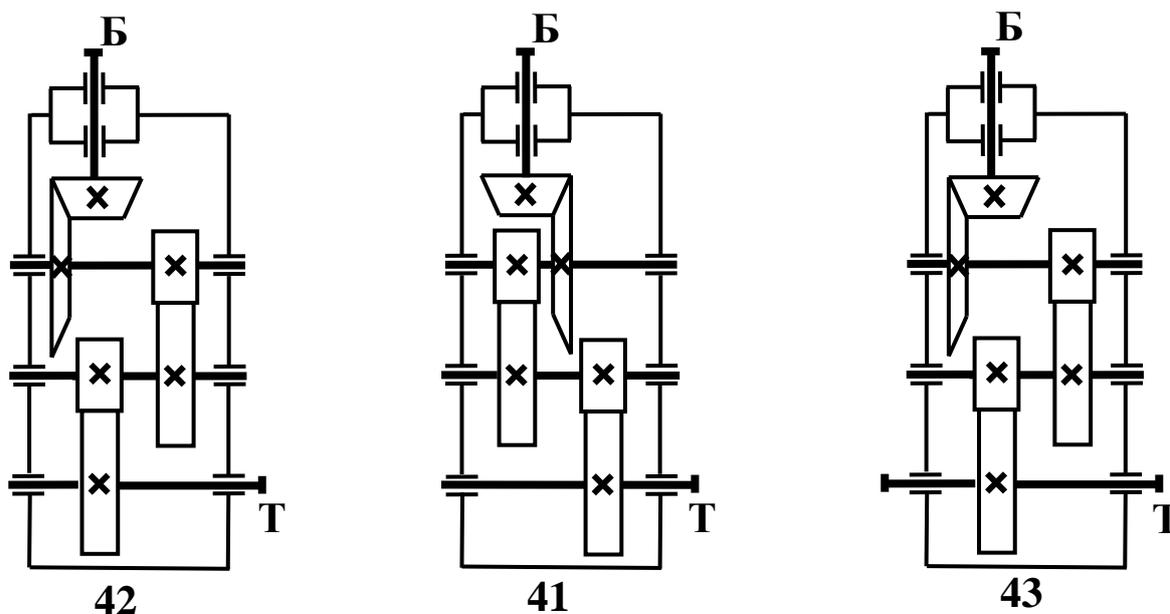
Основные схемы трёхступенчатых коническо-цилиндрических редукторов
